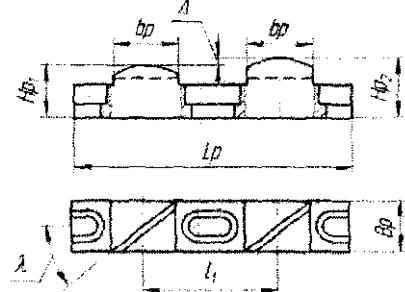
Конструкция резца-зуба развёртки со сдвоенными безвершинными зубьями с разными диаметрами
